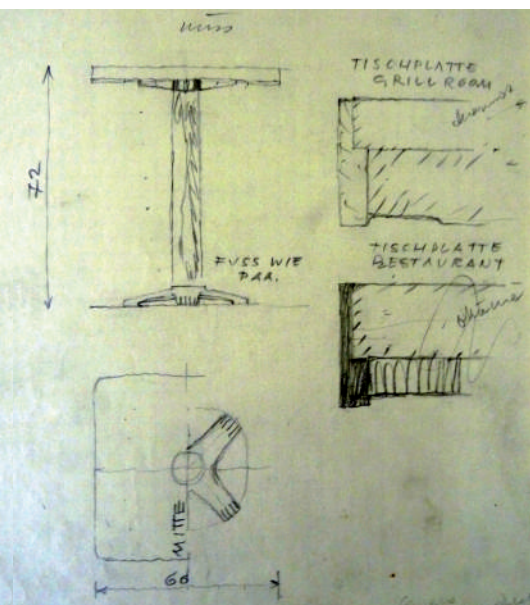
(oben links): *Arabia am Kohlmarkt*, Schnitt, Grundriss und Details der Tische, Entwurfszeichnung, Oswald Haerdtl, 1950.
